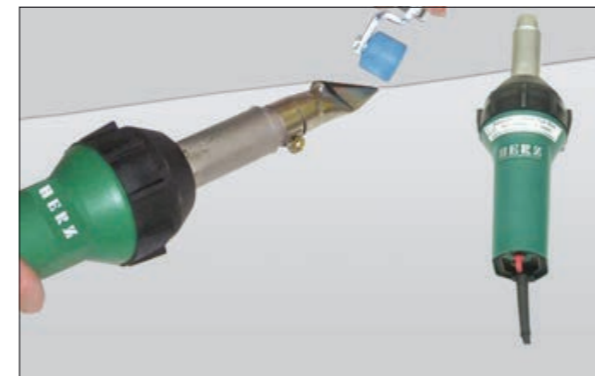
Ручное сварочное оборудование
